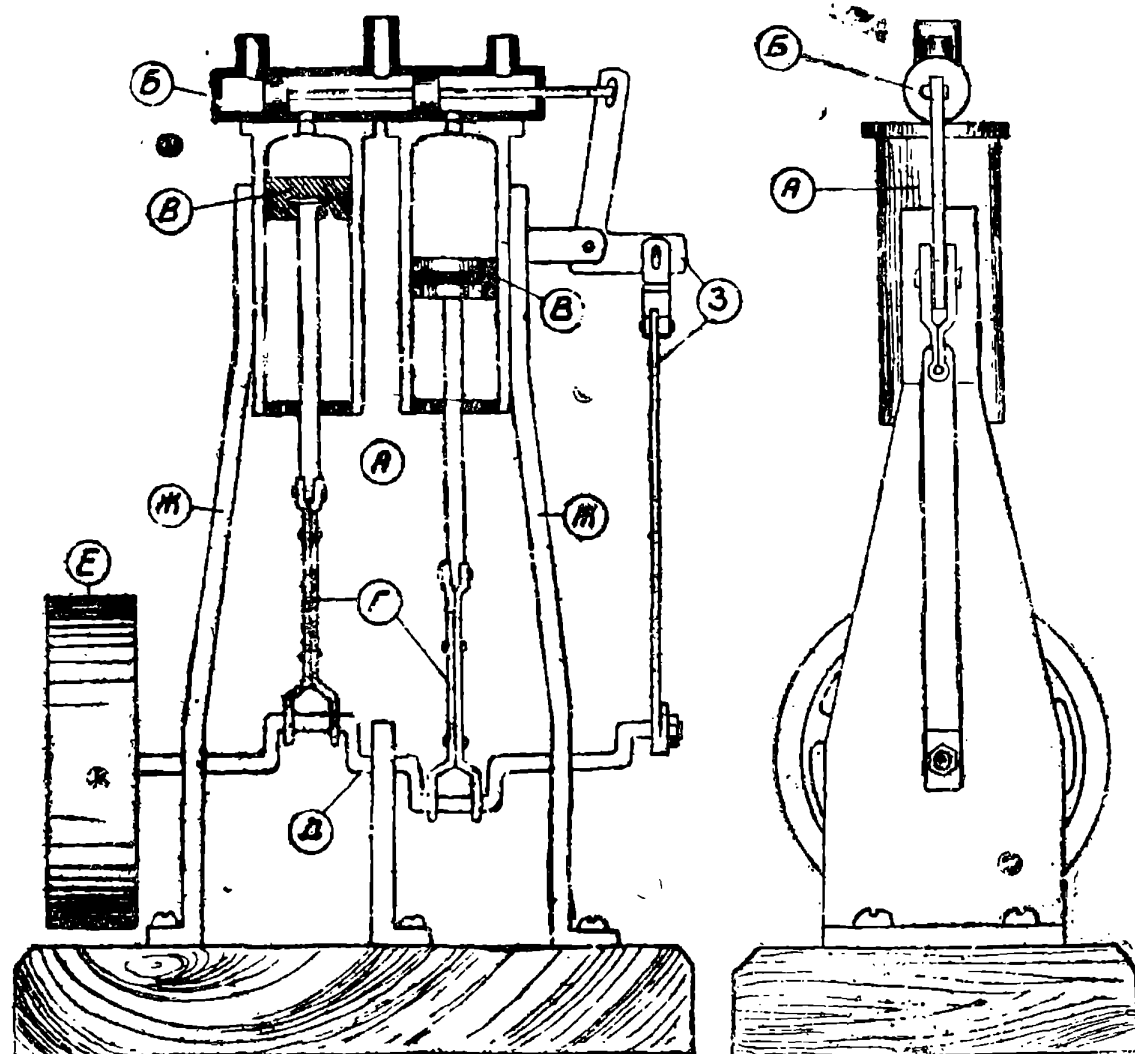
Разрез и боковой вид паровой машины. А — цилиндр из ружейных патронов, Б — золотник, В — поршень с уплотнительным жолобком, Г — шатуны из полосок жести, Д — кривошип, Е — маховик, Ж — боковые стойки из кровельного железа, З — рычаги,двигающие поршни золотника
